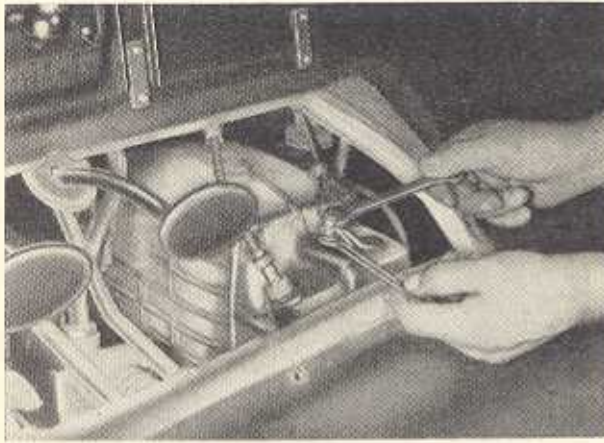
Abklemmen des Seilzuges für die Freilaufperre
